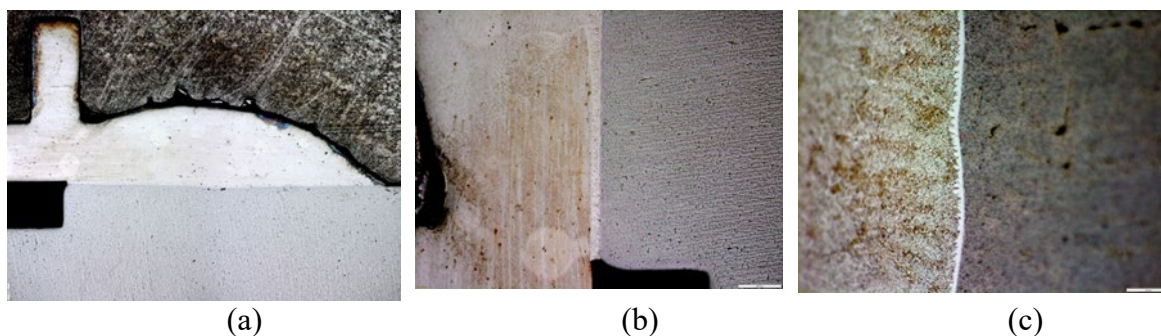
Шлиф нахлесточного сварнопаяного соединения: (a)- общий вид соединения; (b)- сварнопаяный шов; (c)- интерметаллидная прослойка толщиной 3-5 мкм
